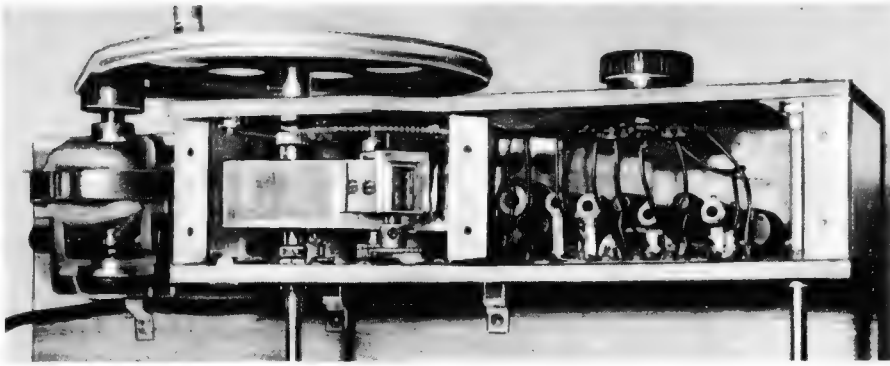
Aufsicht auf die Wickelmaschine ohne Deckblech
